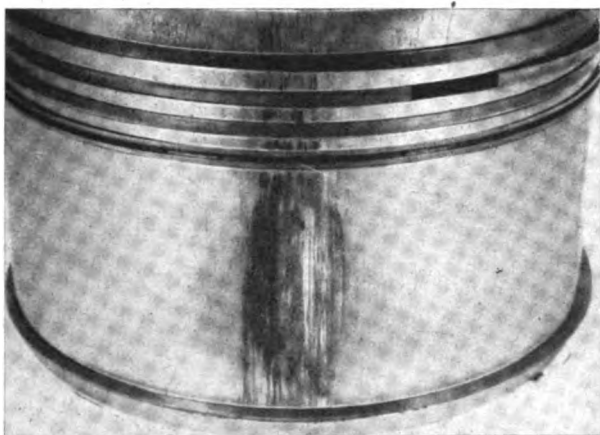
Kolben mit zuerst an der Lauffläche aufgetretener Freßstelle; die Kolbenringe sind frei.
